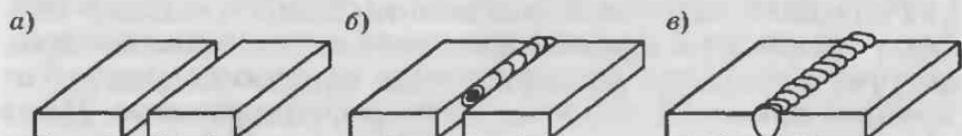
Соединение деталей сваркой плавлением: а — перед сваркой; б — в процессе сварки (сварочная ванна); в — после сварки (сварной шов)
